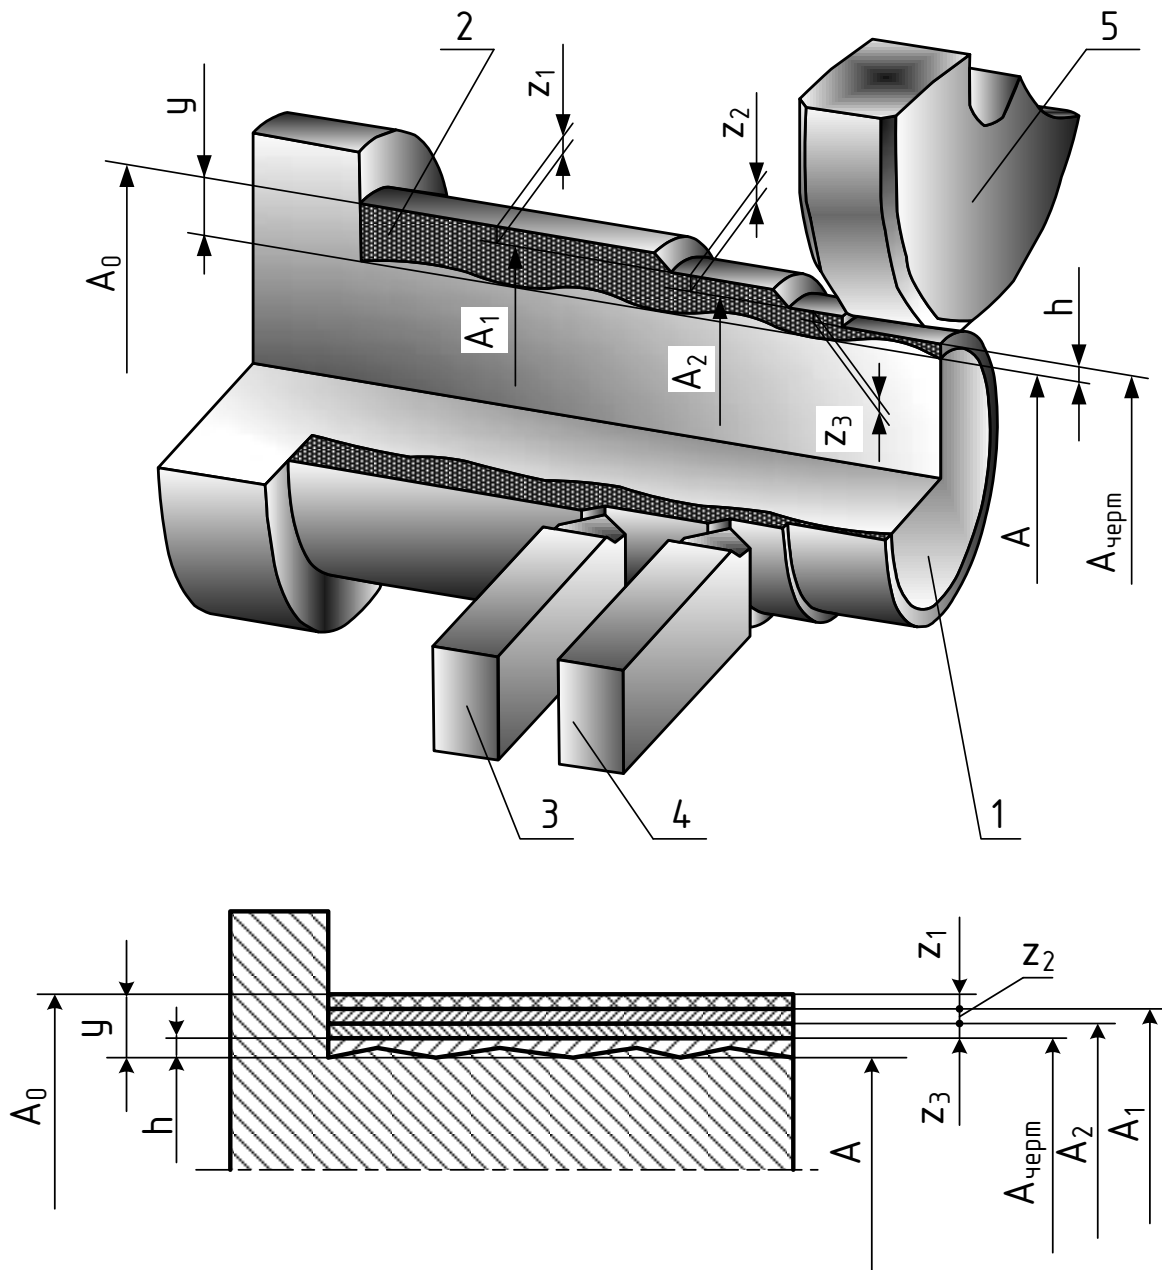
Припуски, толщина нанесенного слоя металла и операционные размеры для восстанавливаемой поверхности вала:
